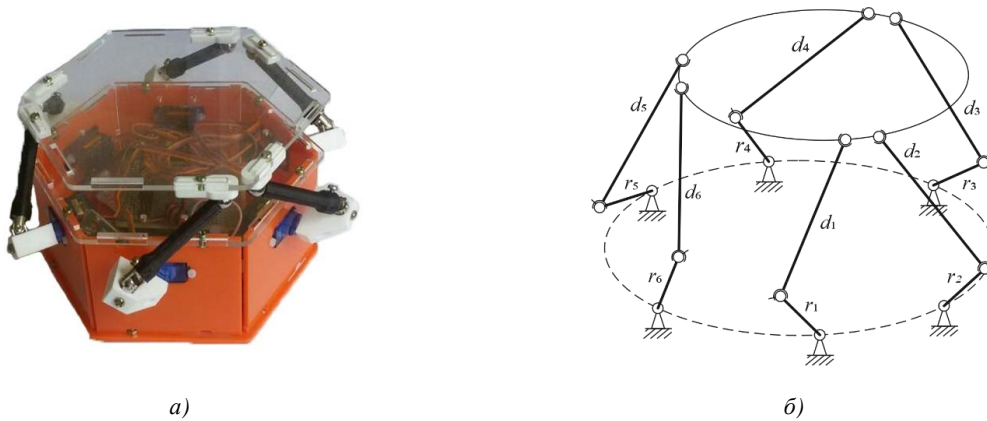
Внешний вид и кинематическая схема предложенного ПМ
